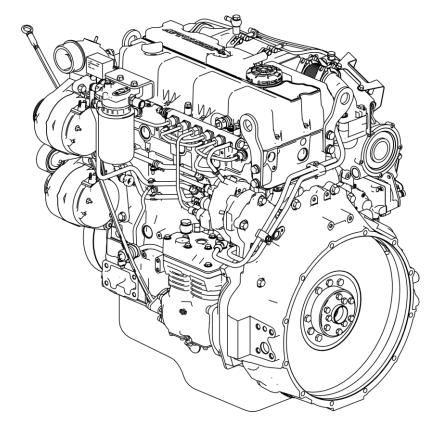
а – Двигатель ЯМЗ-53403 (общий вид слева)
